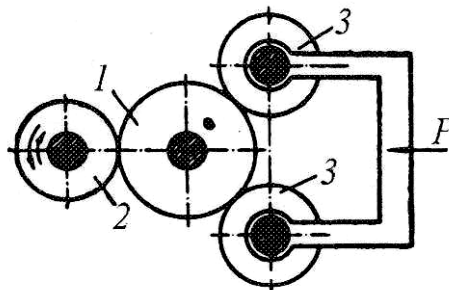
Обкатка зубчастого колеса трьома шестернями-еталонами
